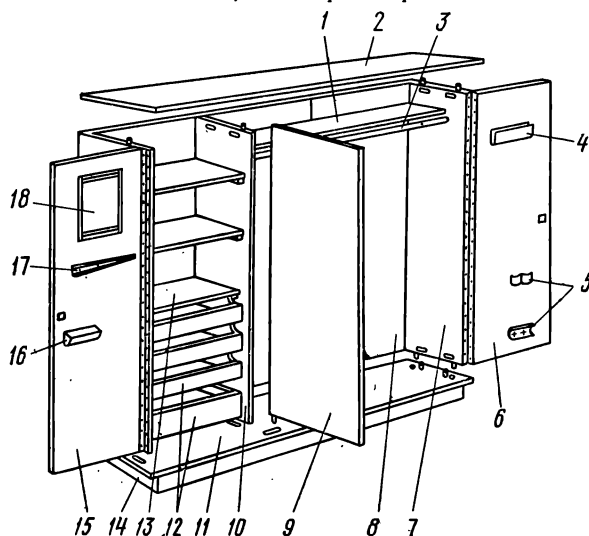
Конструкция трехдверного шкафа для платья и белья:
